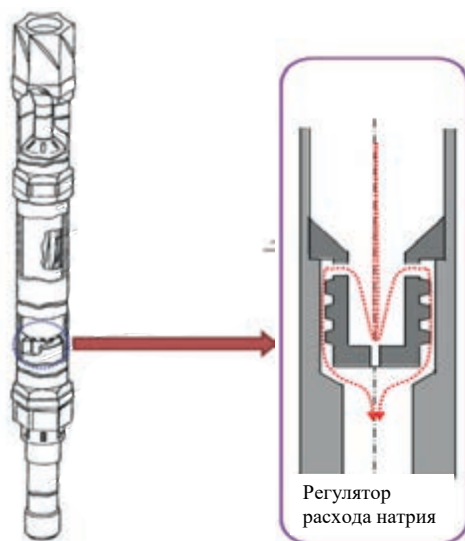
Общий вид конструкции регулирующей сборки реактора и регулятора расхода натрия
